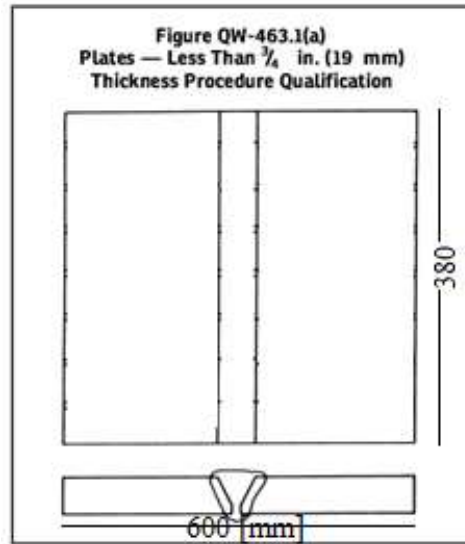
Muestra las dimensiones de las probetas de prueba que deben analizarse para calificar un procedimiento de soldadura.
